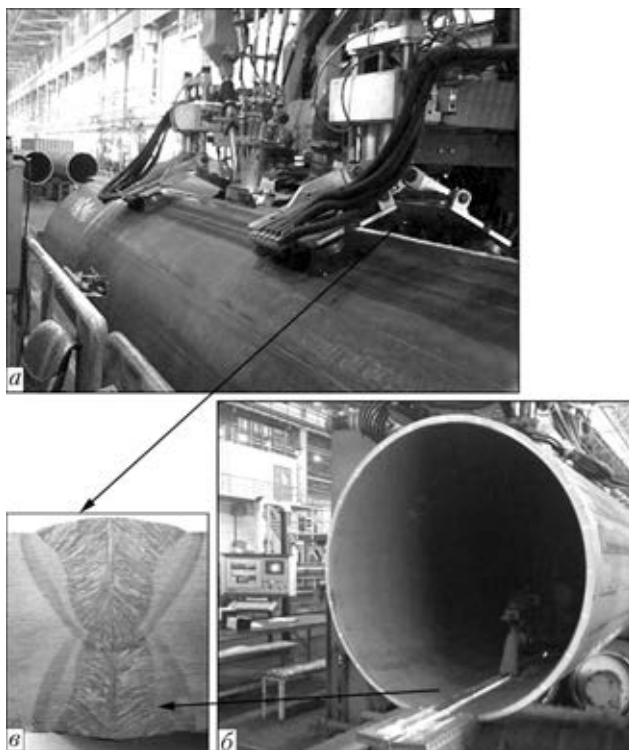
Многодуговая сварка под флюсом трубы диаметром 1420 мм с толщиной стенки 40 мм: *а* — 5-дуговая сварка наружного шва, скорость 110 м/ч; *б* — 4-дуговая сварка внутреннего шва, скорость 100 м/ч; *в* — макрошлиф сварного соединения трубы
